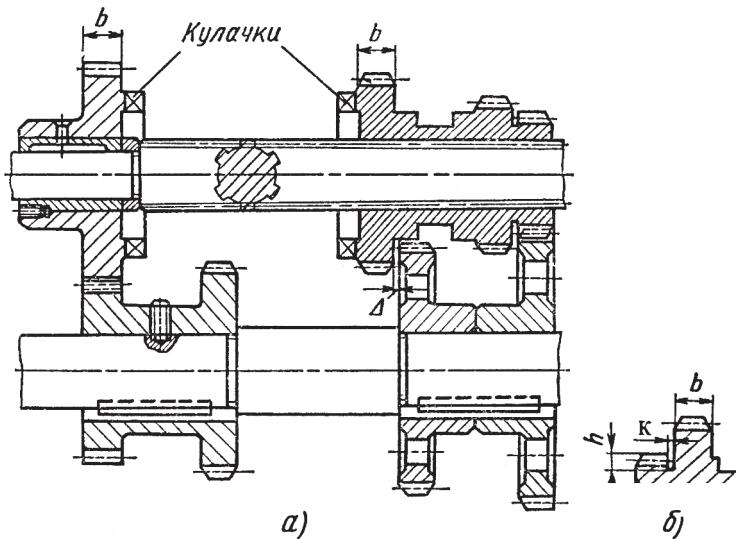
Конструкция коробки передач с блоком шестерен и кулачковой муфты
